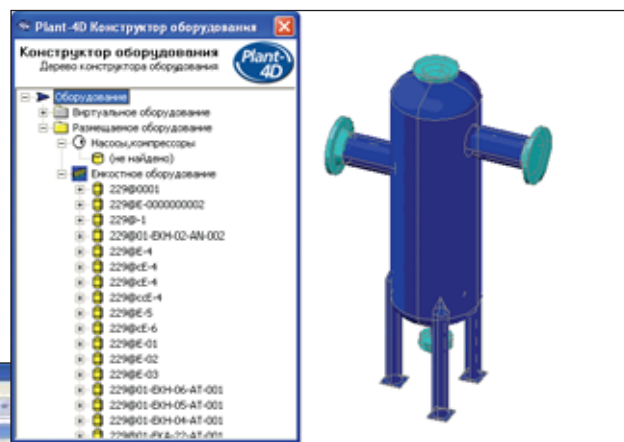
Конструирование нестандартного оборудования в модуле PLANT-4D Конструктор оборудования (Equipment)
